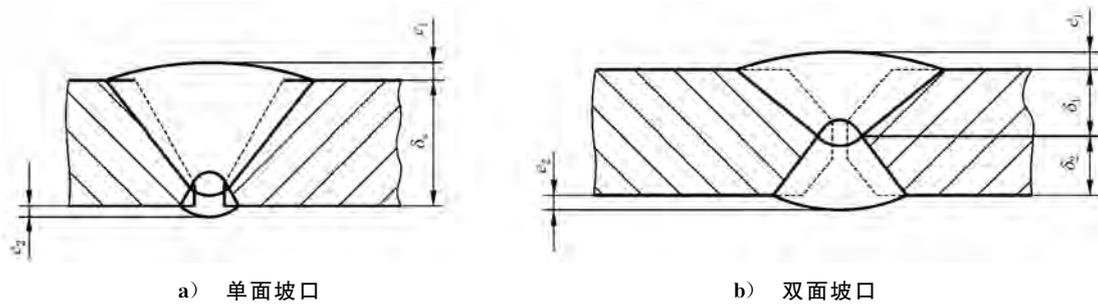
A 类、B 类焊接接头的焊缝余高
